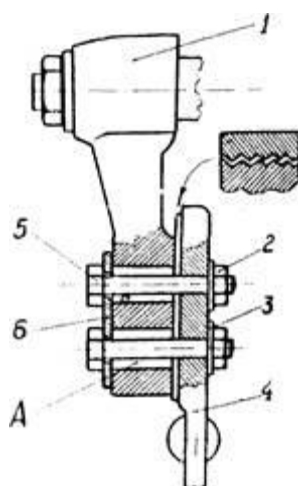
Приводной рычаг механизма качающейся шайбы
